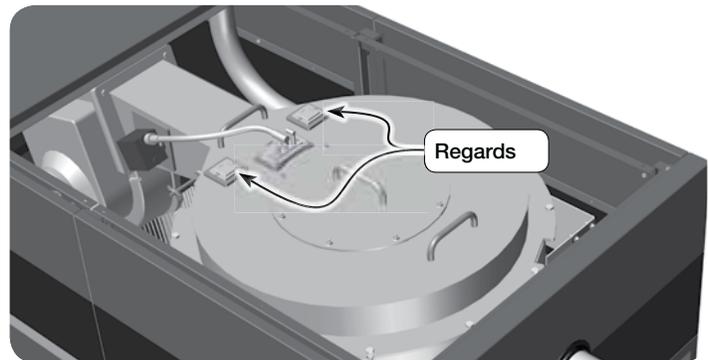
Plaque de d'accès prête pour la dépose et le remplacement du brûleur
